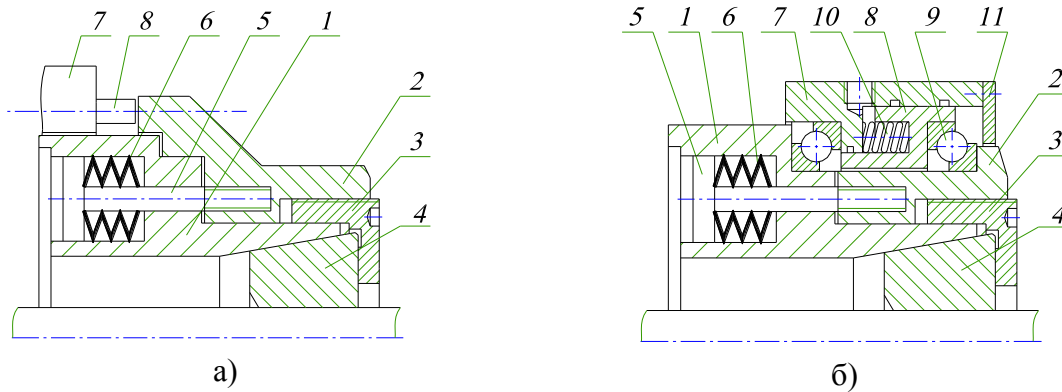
Затискні пристрої цангового типу для токарної обробки з інтегрованими пружинними приводами затиску та гідравлічними приводами розтиску
